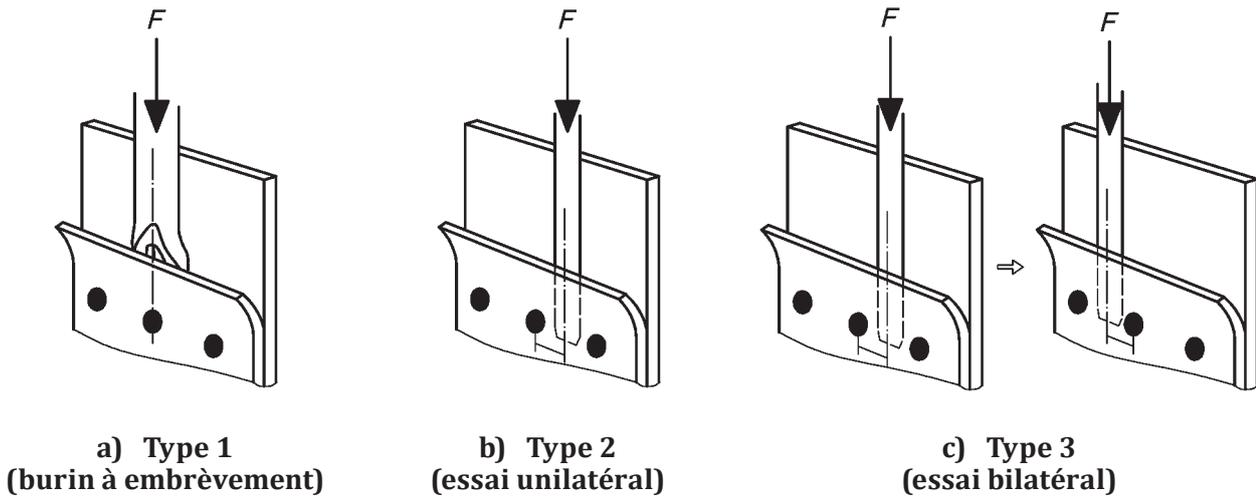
Essai au burin sur joints soudés par résistance par points et par bossages
